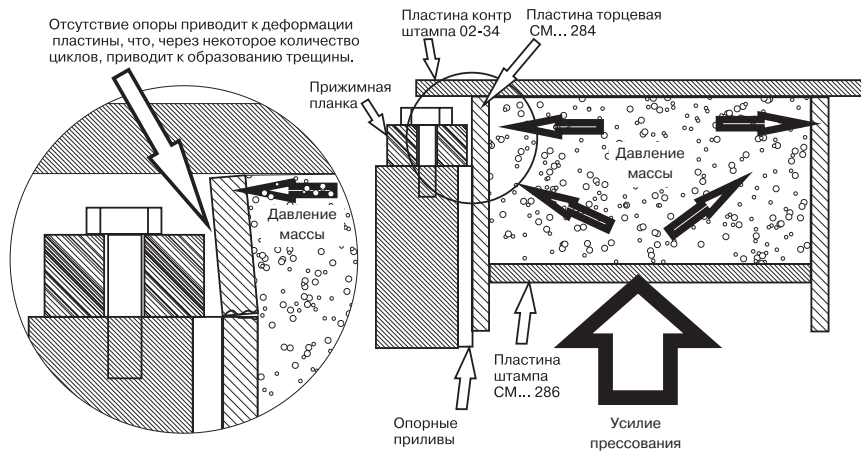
Схема прессования при установке торцевой пластины с большим зазором
